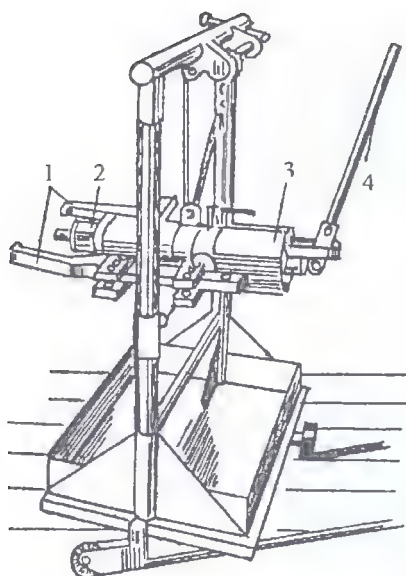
Гидравлический передвижной съемник: 1 — захват; 2 — упор; 3 — плунжерный насос; 4 — рукоятка
